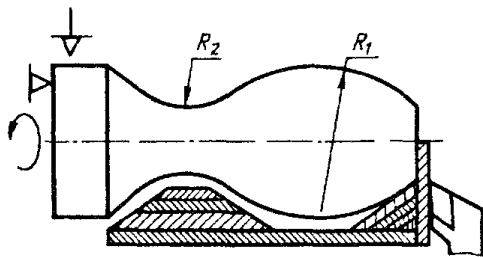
Попереднє оброблення заготовки фасонної деталі
